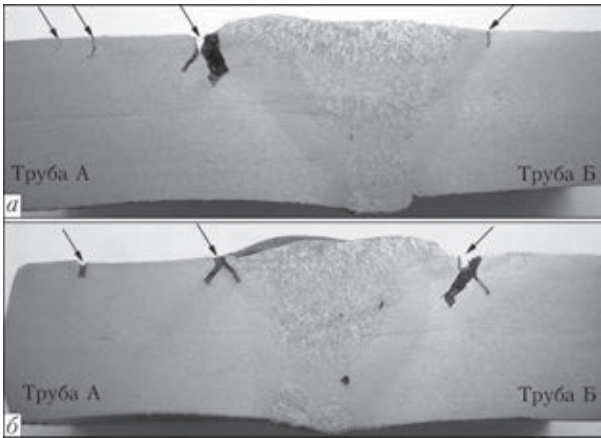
Поперечные макрошлифы кольцевого сварного соединения в зоне повреждения (стрелками показано расположение трещин)
